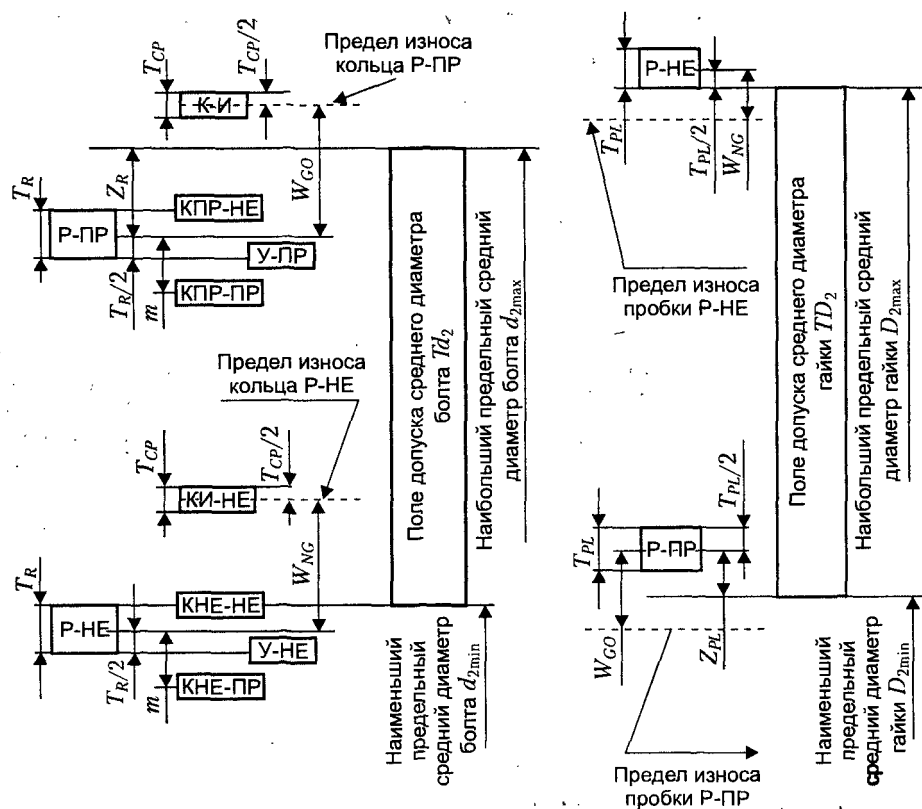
Схемы полей допусков резьбовых калибров
